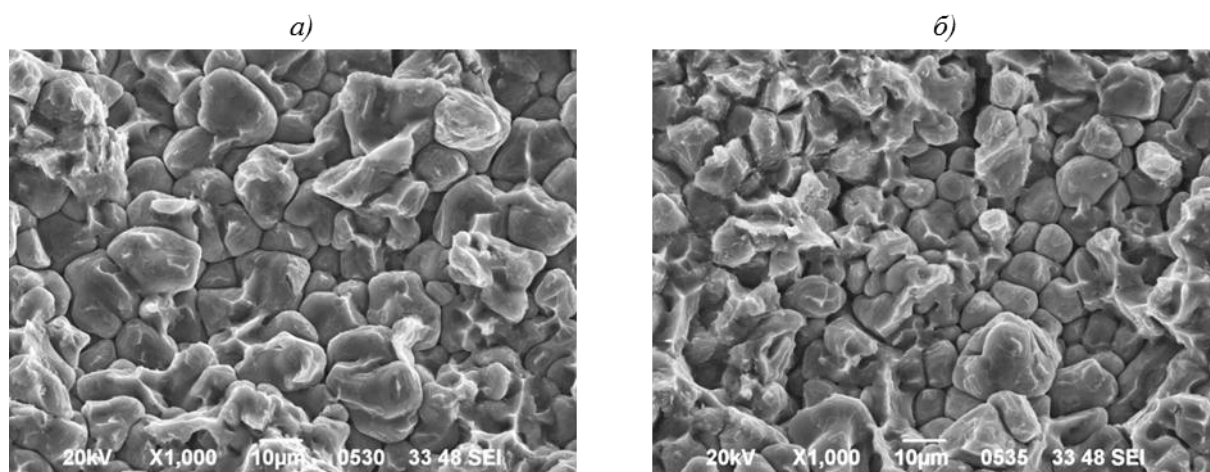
Рыхлота в изломе образцов из сплавов В-1461 (а) и В-1469 (б) при лазерной сварке без присадки
